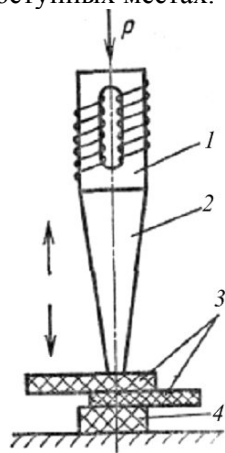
Схема ультразвуковой сварки пластмасс:
